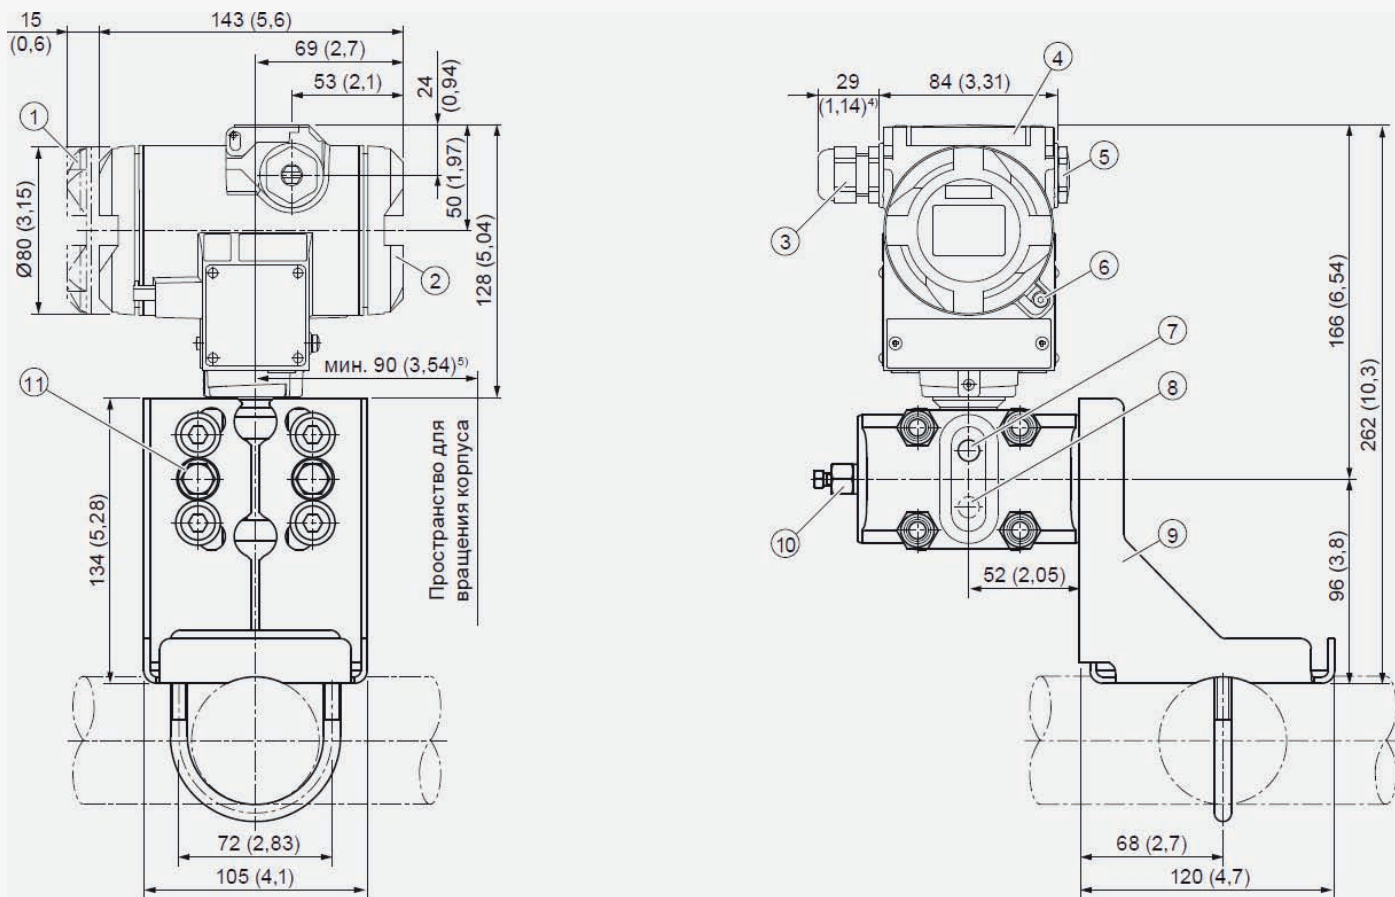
Измерительный преобразователь КМ35 в корпусе дифференциального давления, размеры в мм (дюймах)
